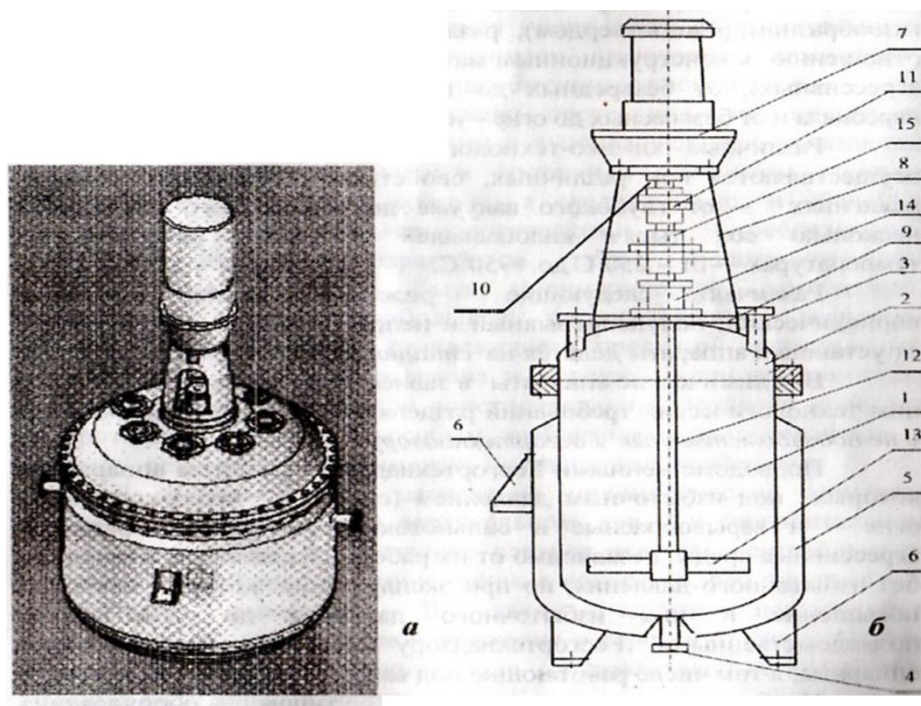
Конструкция типового химического аппарата: а - общий вид; б - схема
